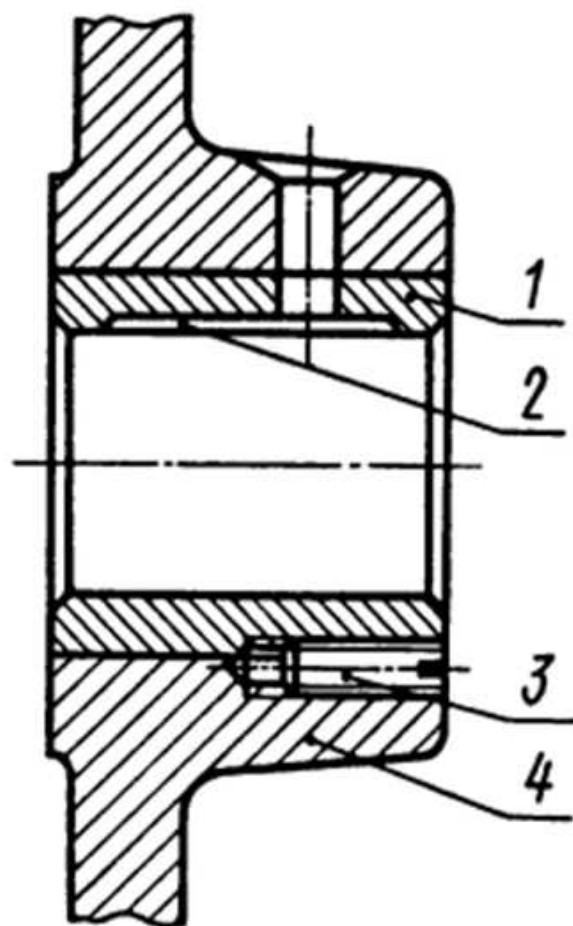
Неразъемный подшипник, встроенный в станину машины:
